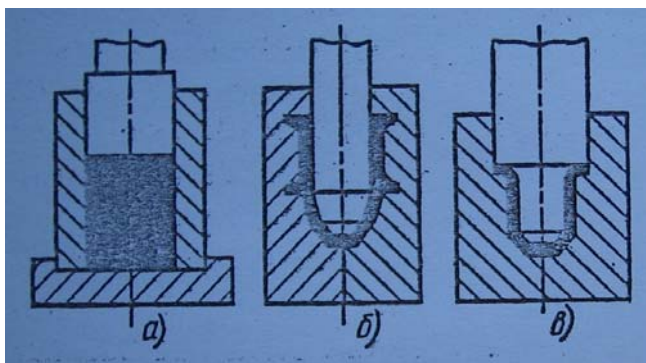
Схема кристаллизации под давлением поршня (а), штамповка из расплава в закрытой (б) и открытой (в) формах.
